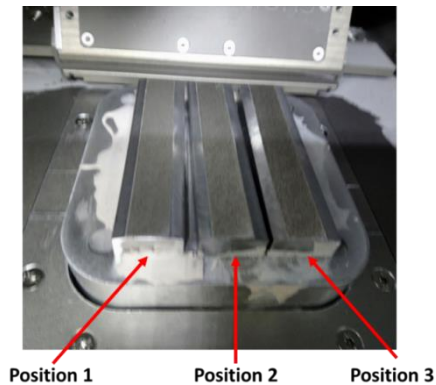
Emplacement des échantillons de fatigue sur le plateau de fabrication SLM pour la fabrication des revêtements : configuration pour 3 échantillons par fabrication
